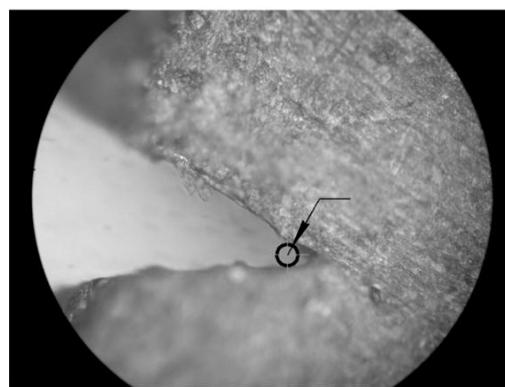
Фотография свинцового слепка режущей кромки ножа:
